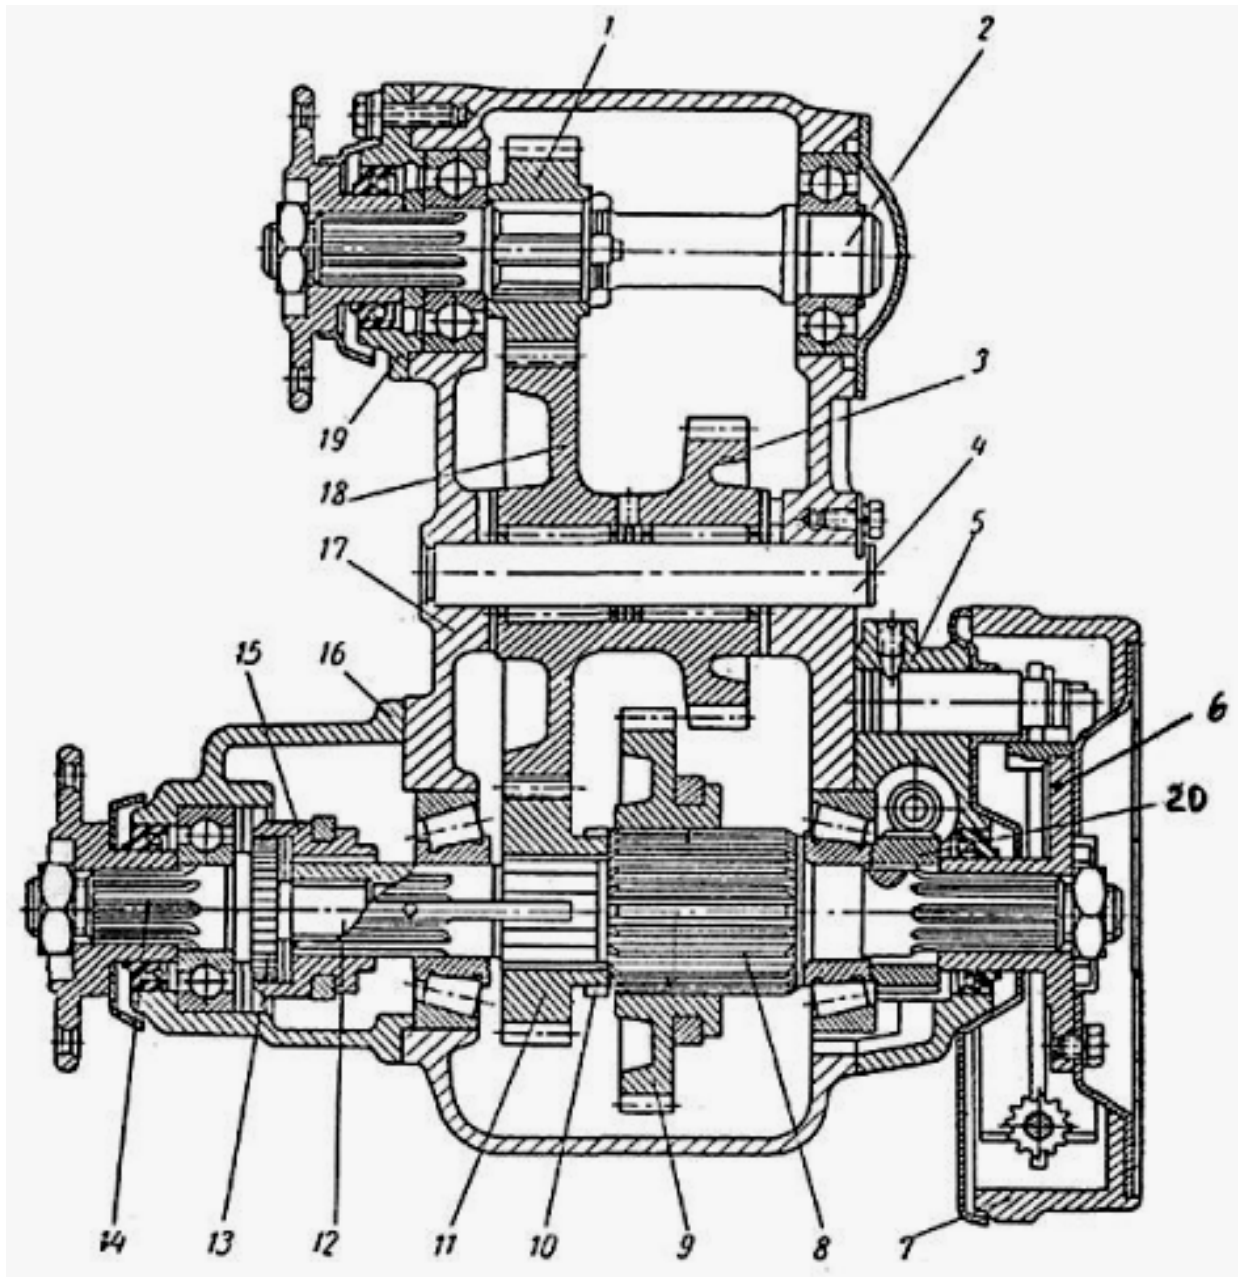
Раздаточная коробка автомобиля с двумя ведущими осями: 1 - ведущая шестерня; 2 - ведущий вал; 3 - шестерня низшей передачи; 4 - ось; 5 - задняя крышка; 6 - фланец карданной передачи; 7 - барабан центрального тормоза; 8 - ведомый вал; 9 - шестерня; 10 - зубчатый венец; 11 - шестерня высшей передачи; 12 - втулка; 13 - зубчатый венец; 14 - вал переднего моста; 15 - муфта; 16 - передняя крышка; 17 - картер; 18 - передняя промежуточная шестерня; 19 - крышка
